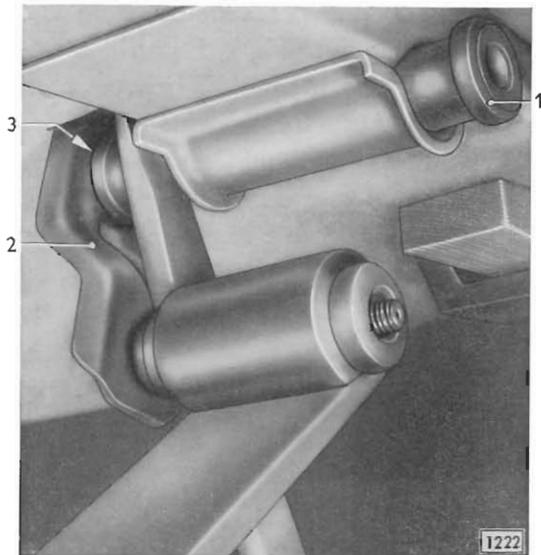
An der linken hinteren Federaufhängung Lasche mit Gehängebolzen aus Aufnahme im Rahmenlängsträger und aus Federauge herauszwingen
